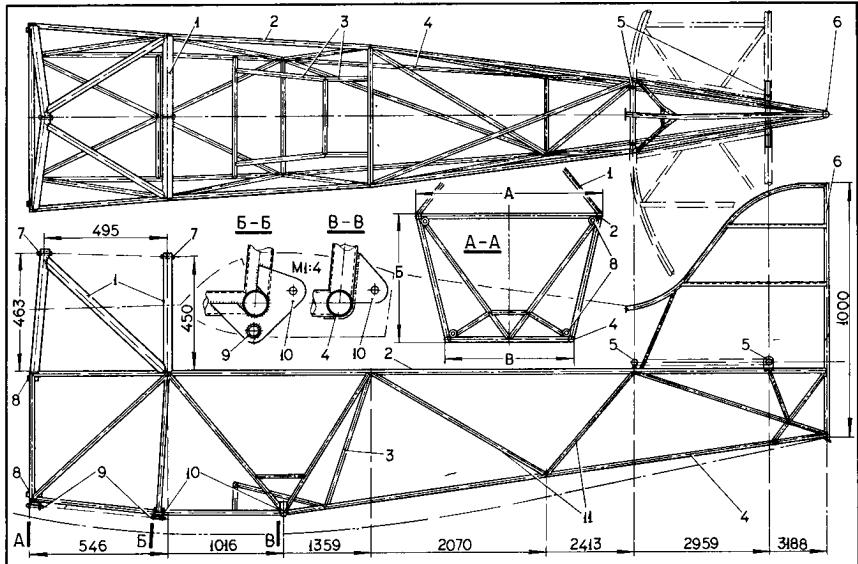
Стальная сварная ферма фюзеляжа самолета «Питтс»:
